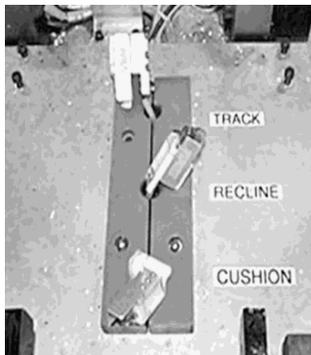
Dispositivo de sujeción de cableado en estación de prueba test
